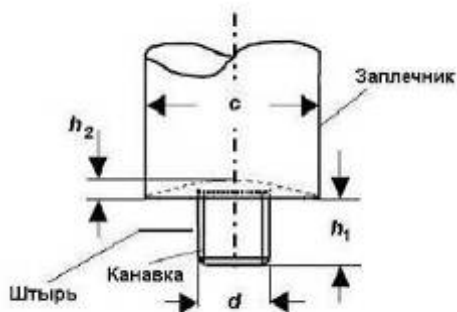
Схема инструмента для наплавки и сварки трением с перемешиванием
